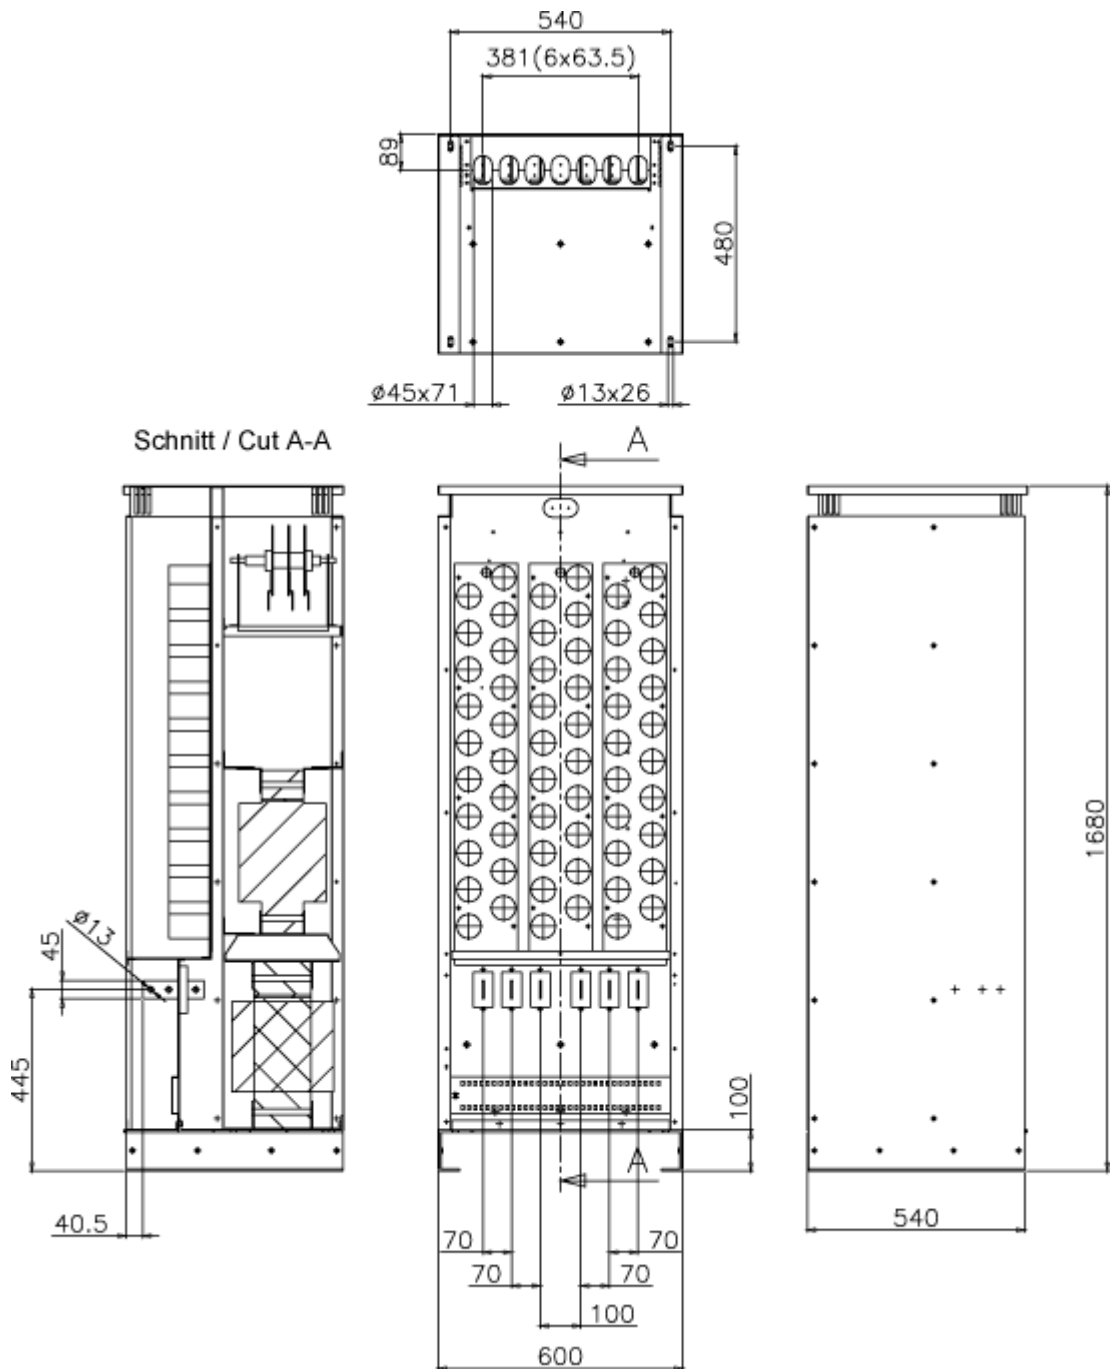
Maßbild Line Harmonics Filter: 6SL3000-0JE36-1AA0, 6SL3000-0JH33-3AA0
